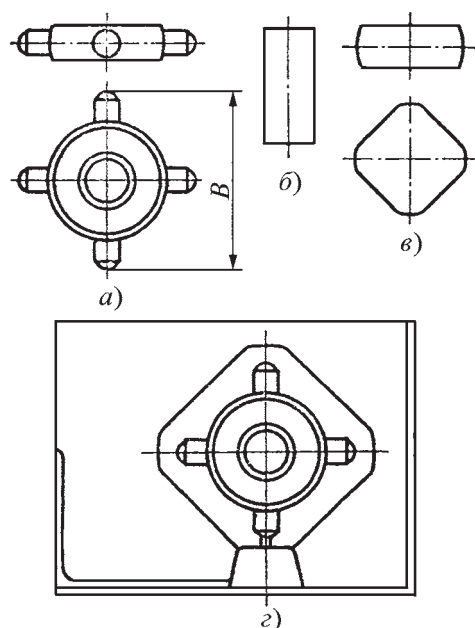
Штамповка крестовины из осажженной заготовки с деформированием на квадрат (в плане) в одном окончательном ручье:
